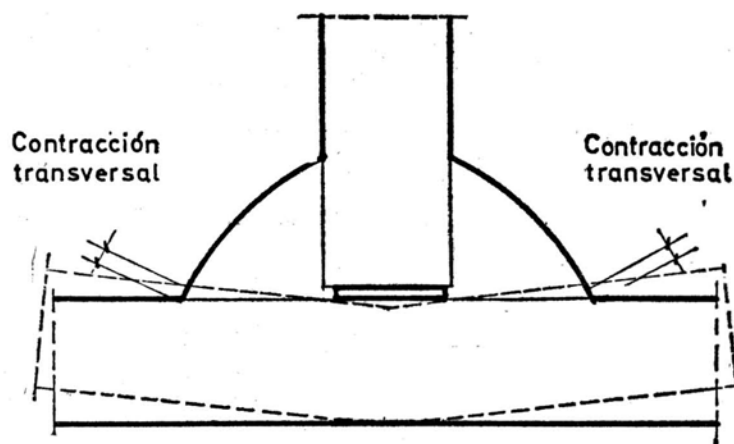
ABARQUILLAMIENTO POR UNA SOLDADURA EN ANGULO DOBLE
